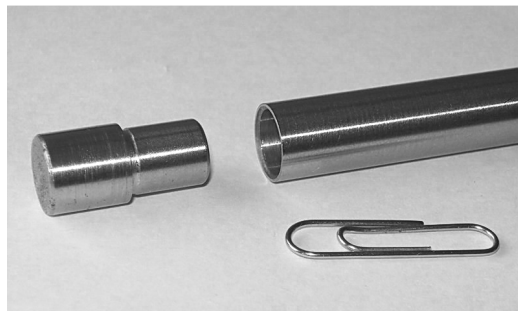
Фотография заглушки и трубки твэла до сварки
